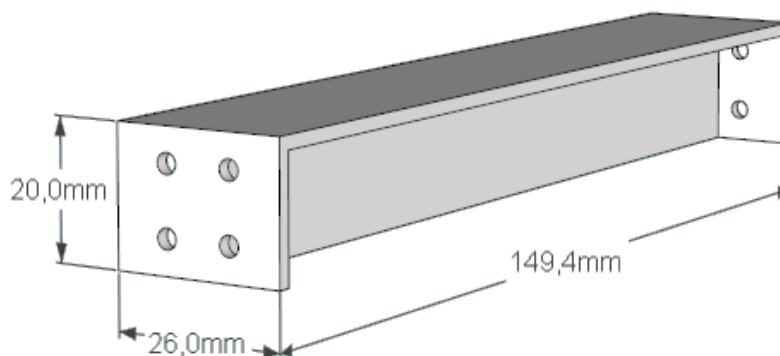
Трёхмерный вид детали 2го звена с указанными размерами
